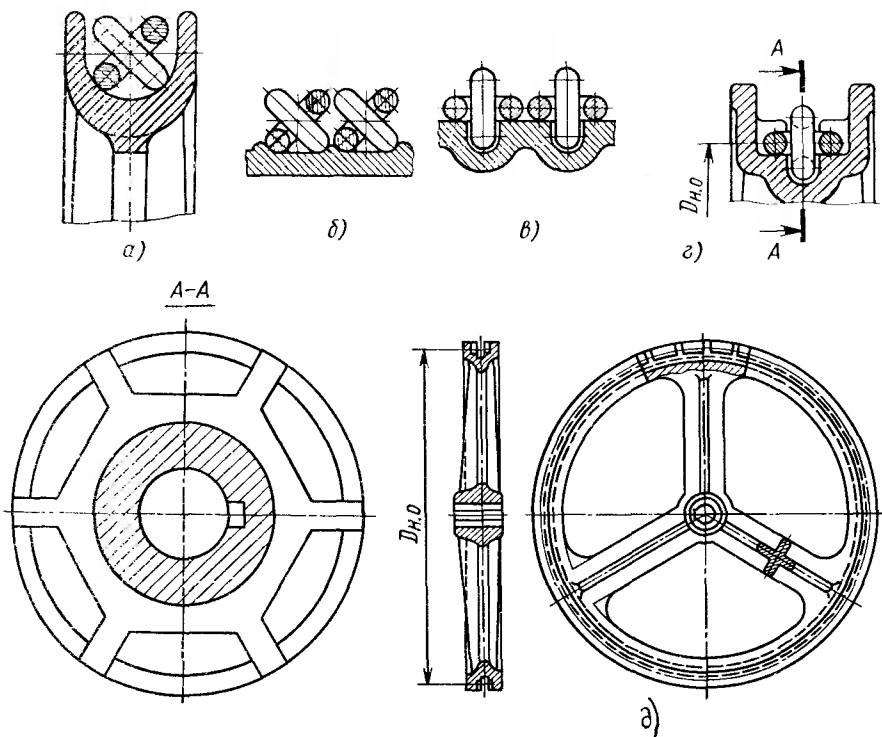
Схемы укладки сварных цепей на различных деталях:
